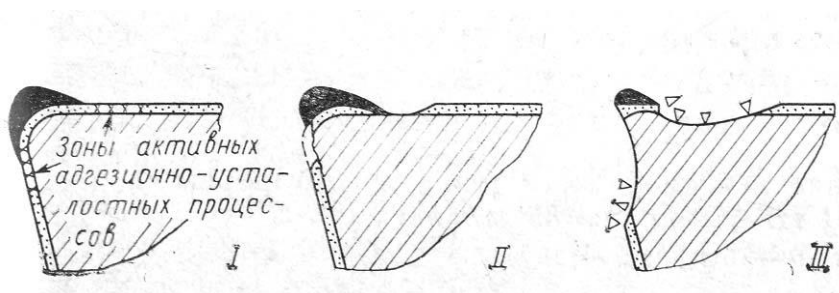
Обобщенная схема развития очагов изнашивания быстрорежущего инструмента с покрытием
